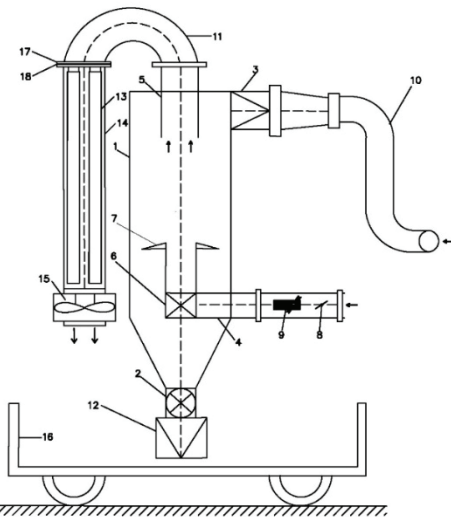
Схема пылеуловителя ВЗП с фильтрующими рукавами
